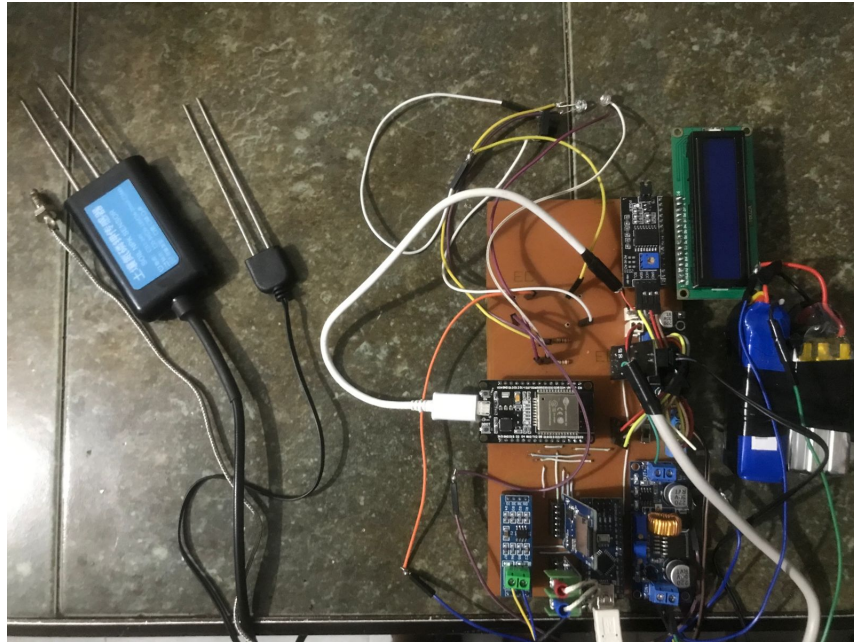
Placa PCB ensamblada. Fuente: Propia
